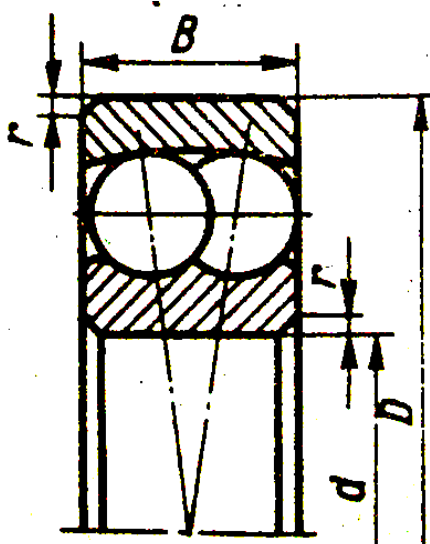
Подшипник шариковый радиальный сферический двухрядный (из ГОСТ 28428-90)
